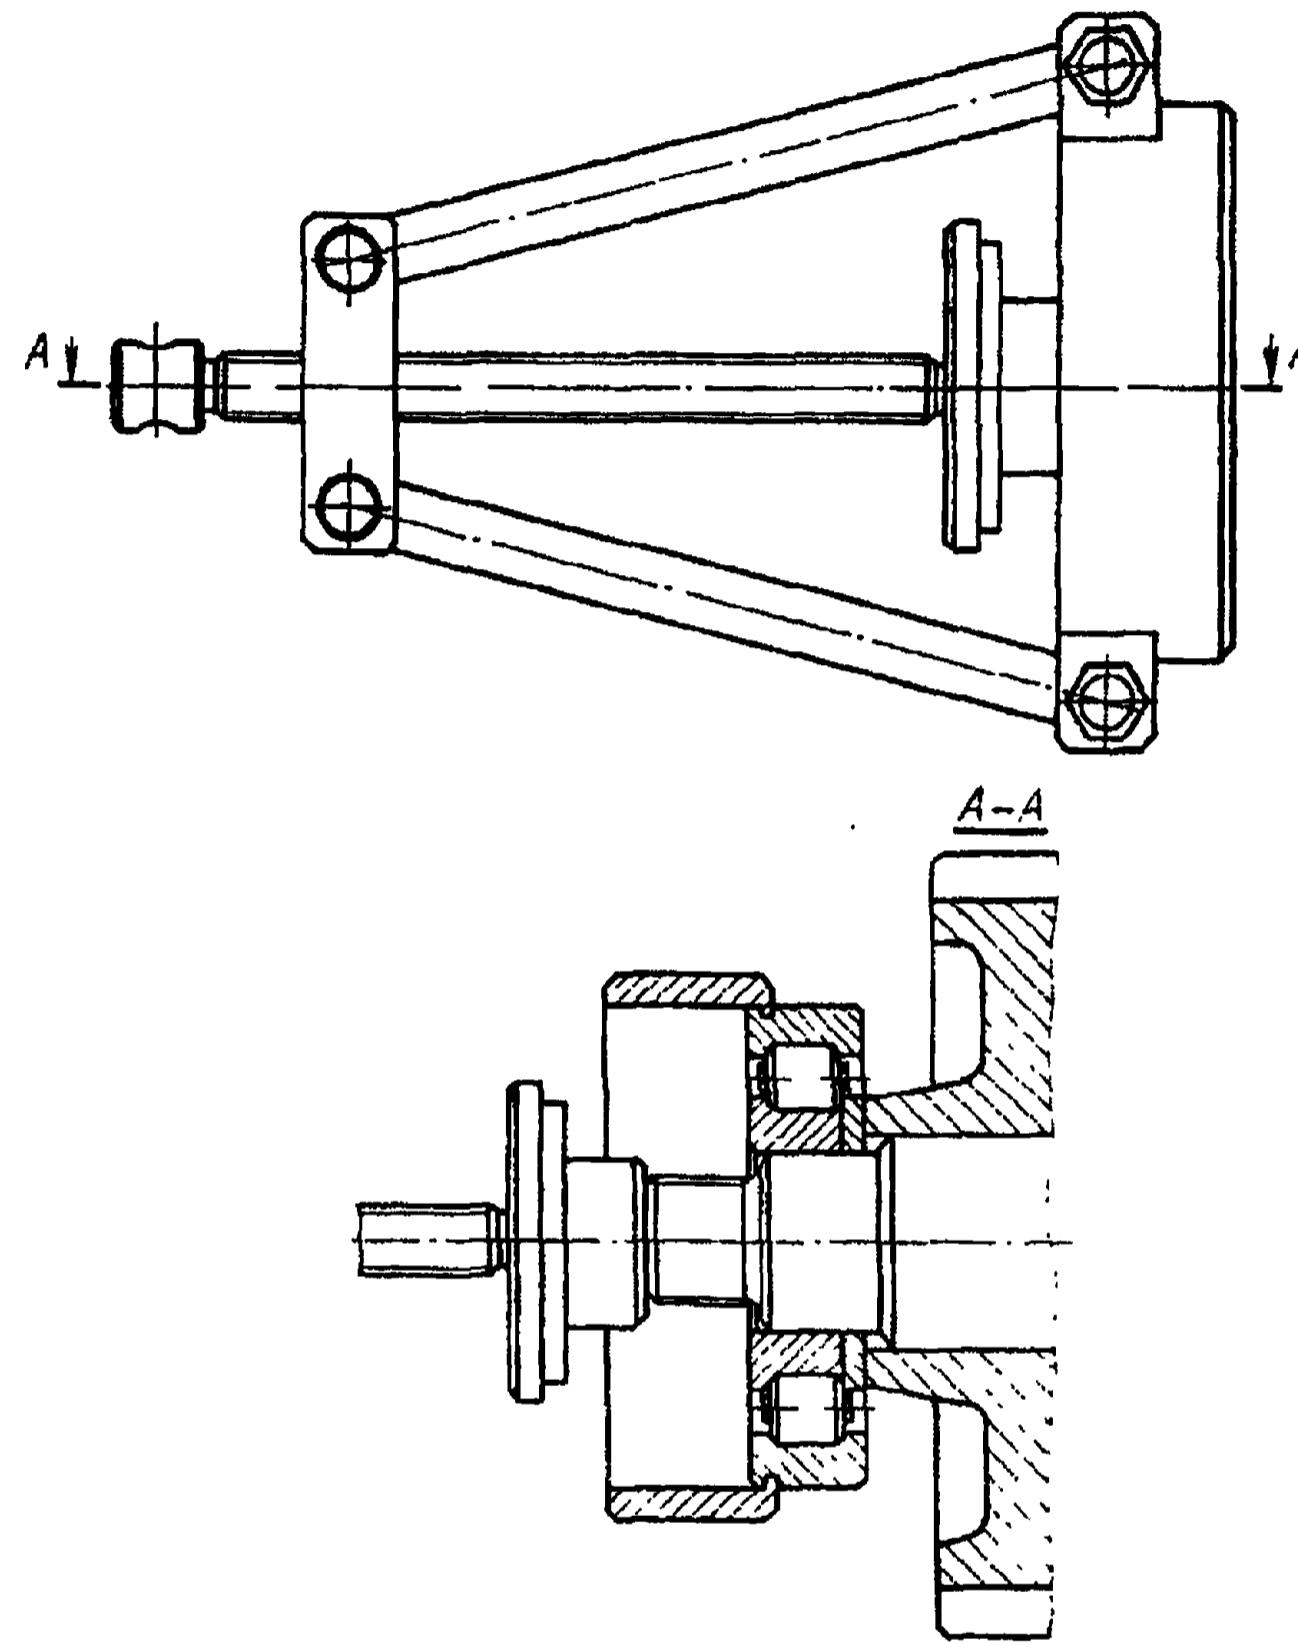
Снятие внутреннего кольца переднего подшипника промежуточного вала
